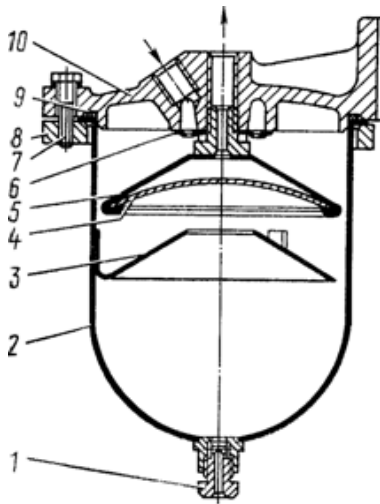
Фильтр грубой очистки топлива: 1 – пробка сливная; 2 – стакан; 3 – успокоитель; 4 – сетка фильтрующая; 5 – отражатель; 6 – распределитель; 7 – болт; 8 – фланец; 9 – кольцо уплотнительное; 10 – корпус
